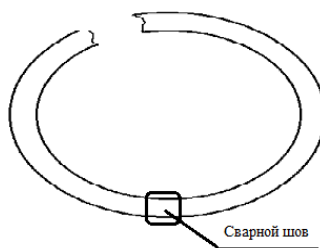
Образец на растяжение сварного соединения после испытания
